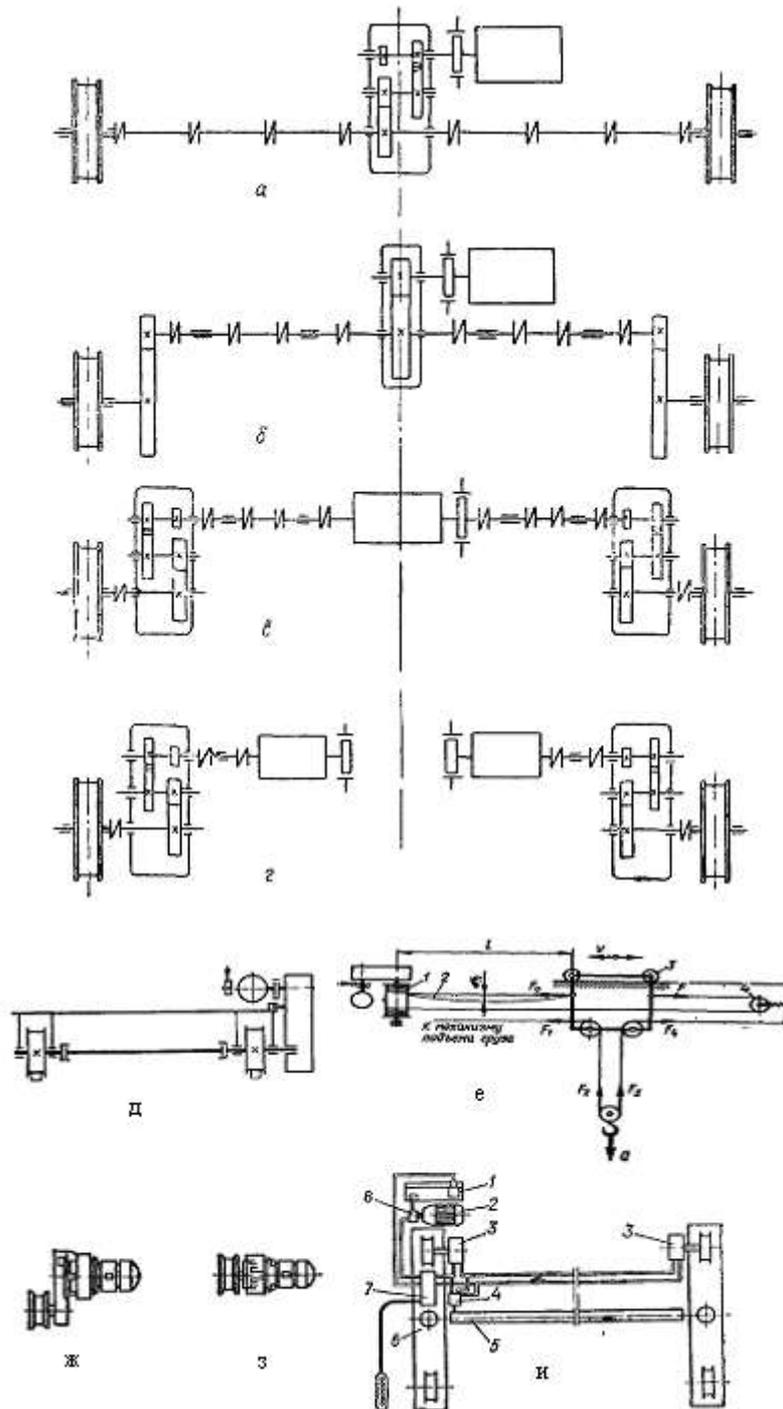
Схемы расположения приводов в механизмах передвижения.
